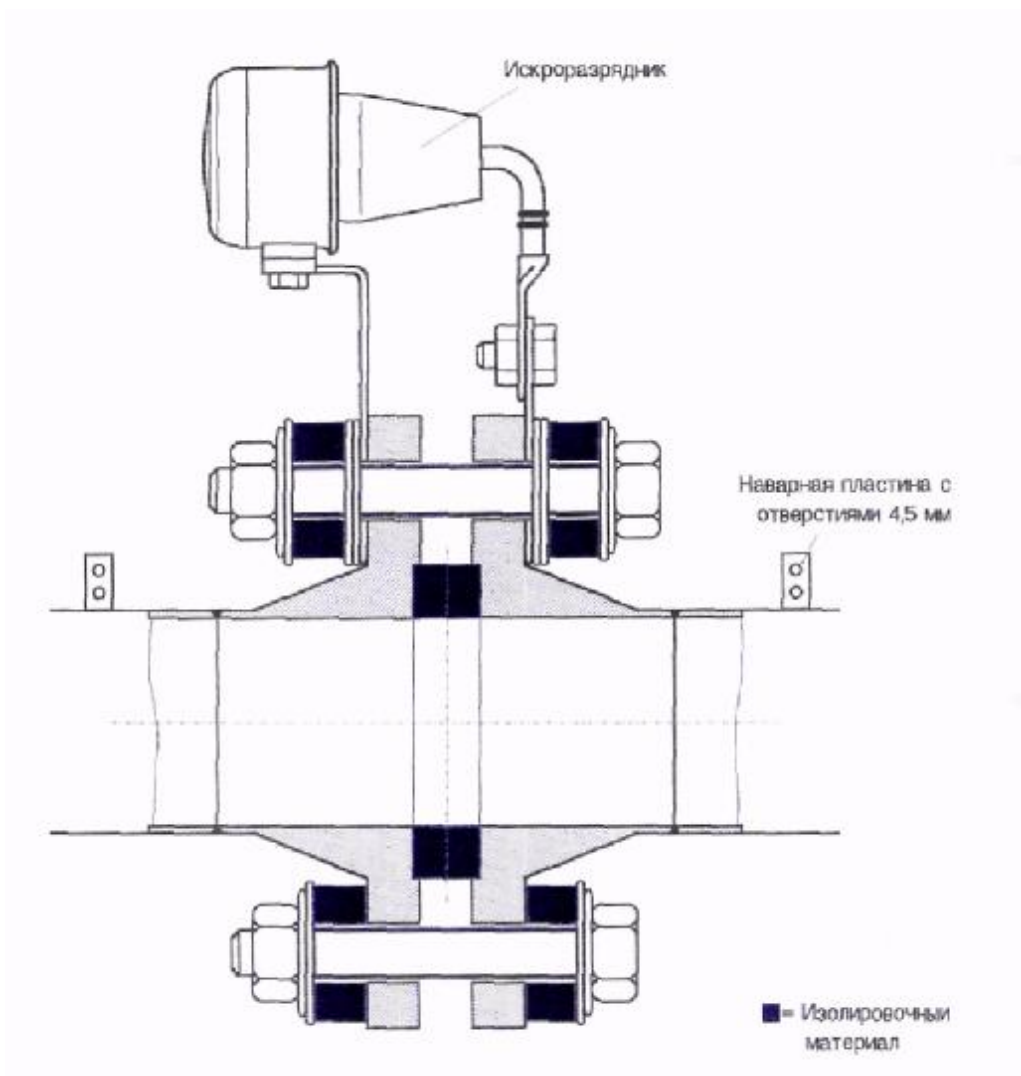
Изолирующая фланцевая пара после установки, с двумя приваренными концами трубы оснащенная искро разрядником и двумя наварными пластинами (для измерений ЭХЗ)
